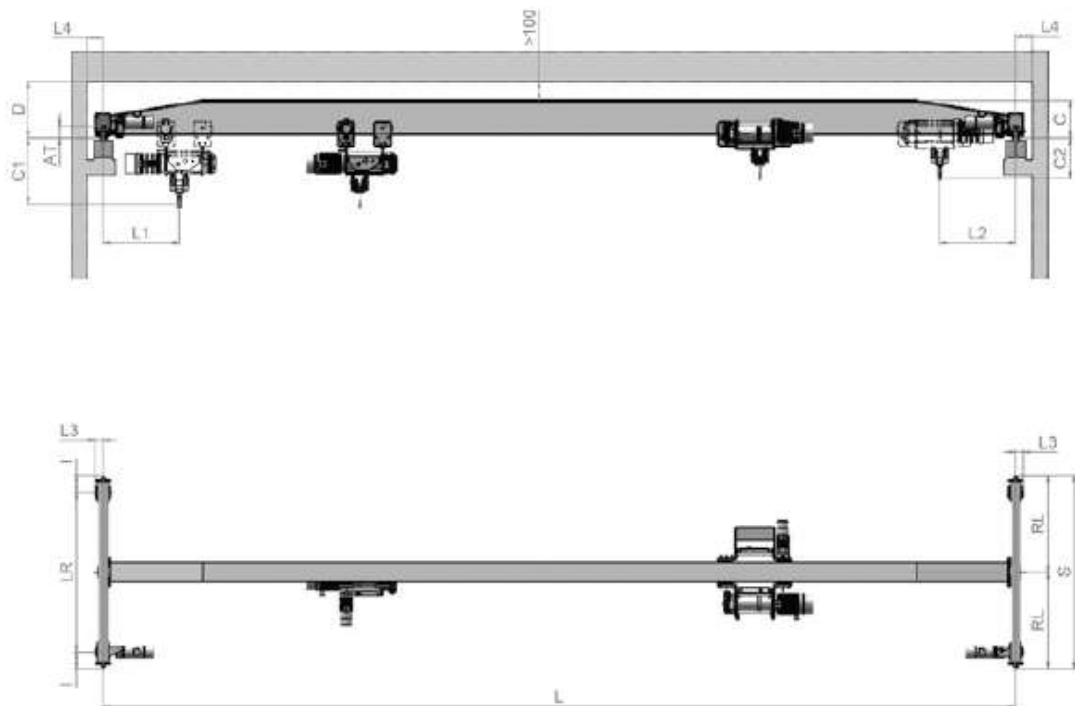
Planta y alzado, respectivamente, del puente grúa (Catálogo Jaso Group)
